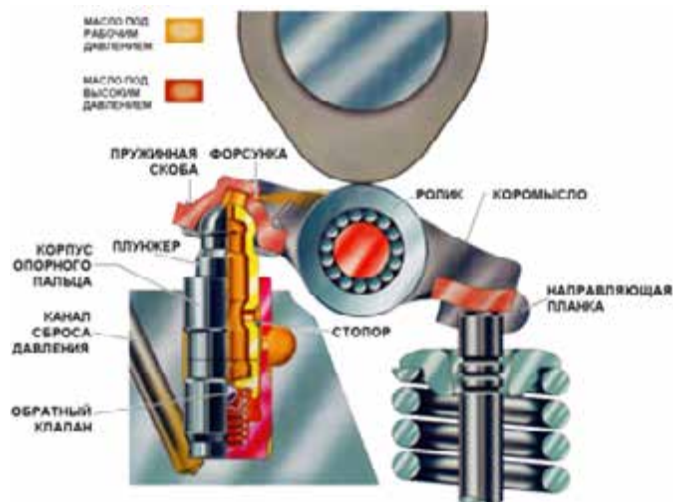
Устройство гидравлического компенсатора, встроенного в опорный палец привода клапана; источник: *INA
